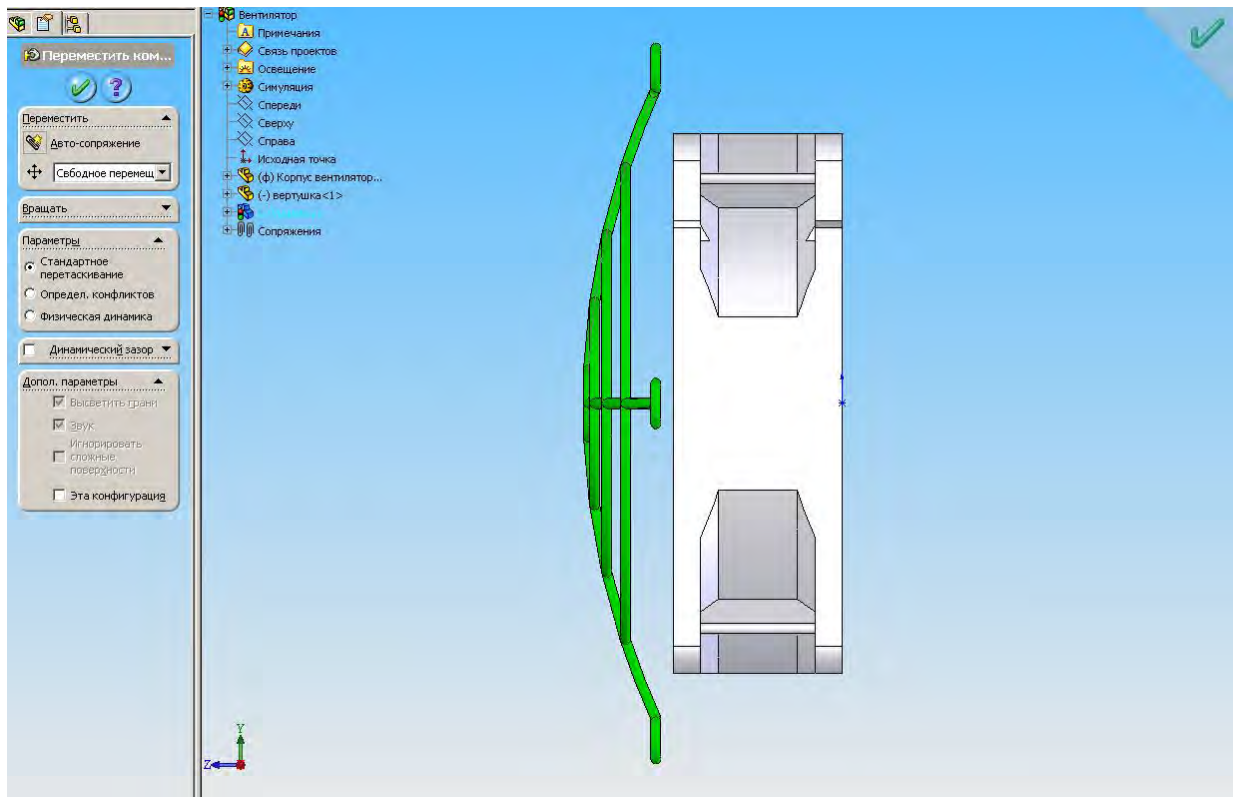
Розташування ґрат перед корпусом вентилятора
